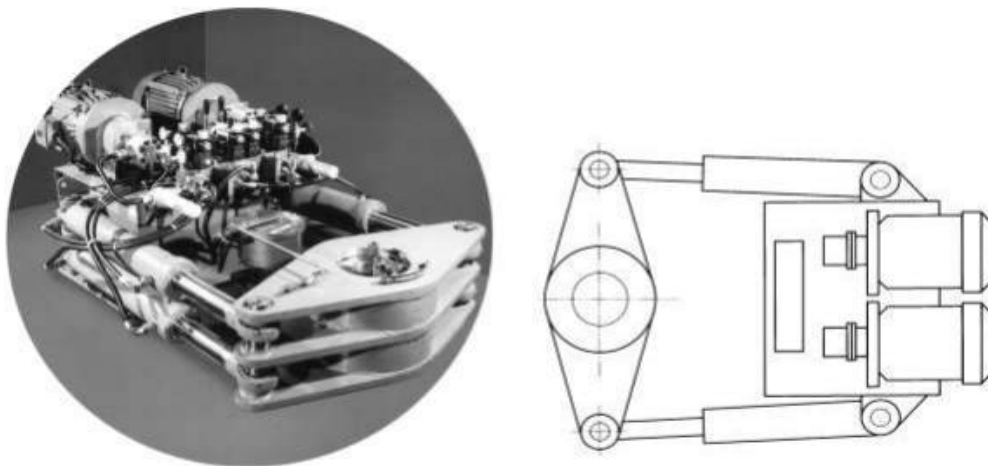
Рулевой привод с качающимися цилиндрами
